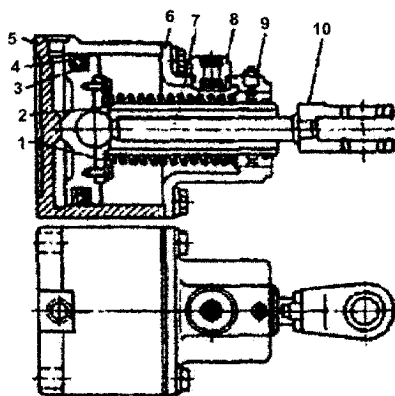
Тормозной цилиндр электровоза 13АРП1: 1 – пружина; 2 – направляющие трубки; 3 – манжетное уплотнение; 4 – поршень; 5 – корпус; 6 – горловина; 7 – шток со сферической головкой; 8 – пробки с фильтром; 9 – шариковая масленка; 10 – вилка.
